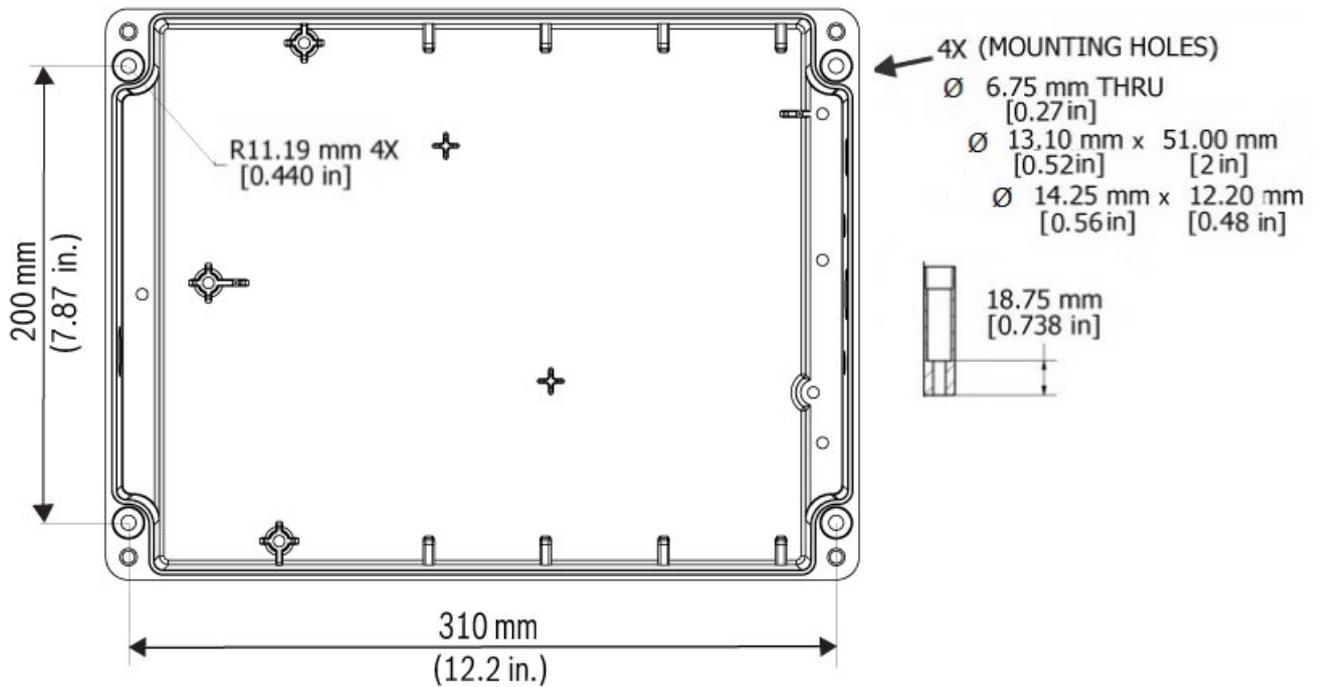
Abmessungen, Befestigungslöcher für VIDEOJET connect 7000
